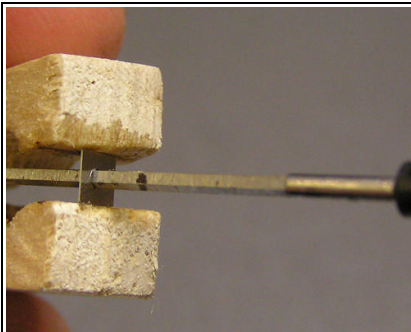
Das Loch auf 1,4mm (= Buchsenaußendurchmesser) aufreiben.
